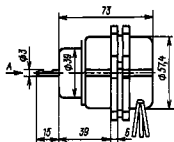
Габаритные и установочные размеры двигателя ДС-1
